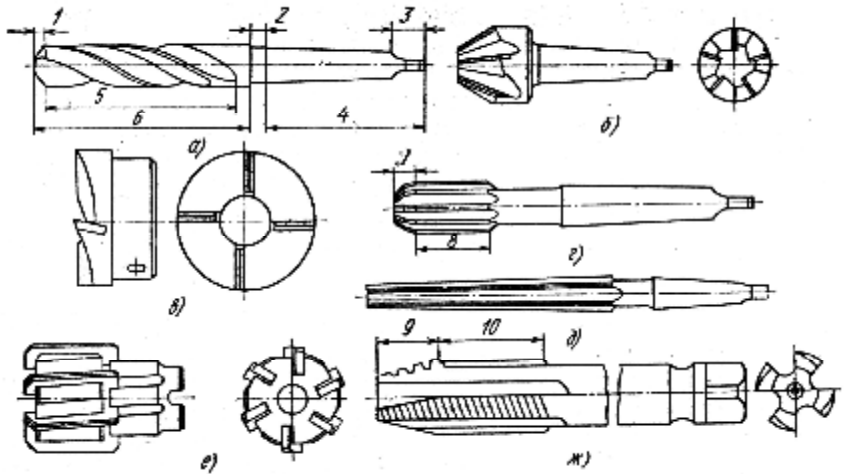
Инструменты для обработки отверстий на сверлильных станках:
